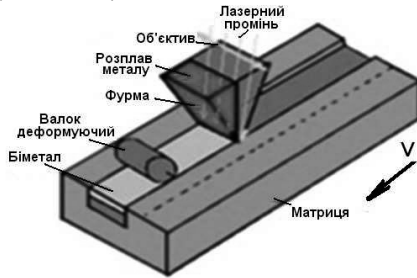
Схема лазерно-ливарного процесу виготовлення біметалів
